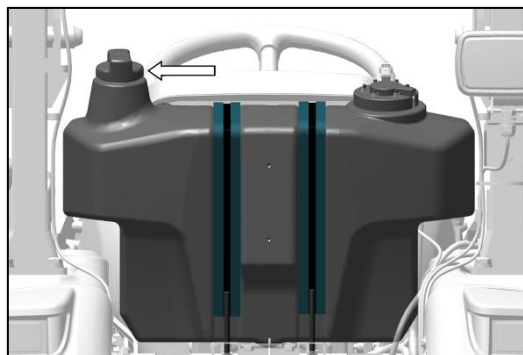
BOUCHON DE REMPLISSAGE DE CARBURANT
